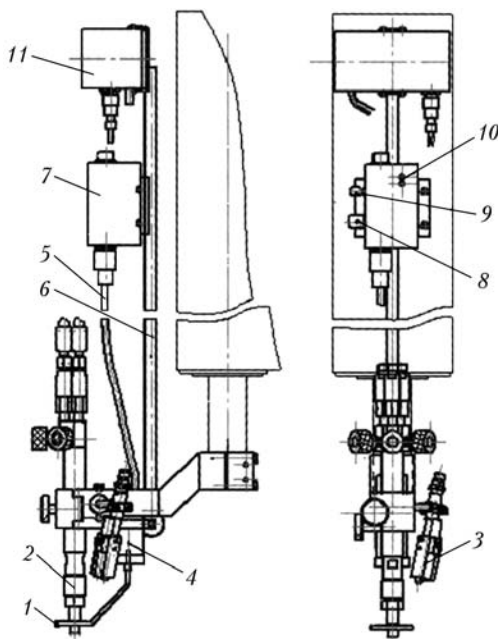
Схема расположения устройств СВР-3М и УПГ-2 на каретке МТР: 1 — одновитковая антенна стабилизатора высоты; 2 — газовый резак; 3 — зажигалка; 4 — корпус датчика стабилизатора высоты; 5 — соединительный кабель стабилизатора высоты; 6 — штанга-держатель; 7 — электронный блок стабилизатора высоты; 8 — ручка плавной установки высоты; 9 — ручка ступенчатой установки высоты; 10 — сигнальные светодиоды; 11 — электронный блок устройства поджига газа
